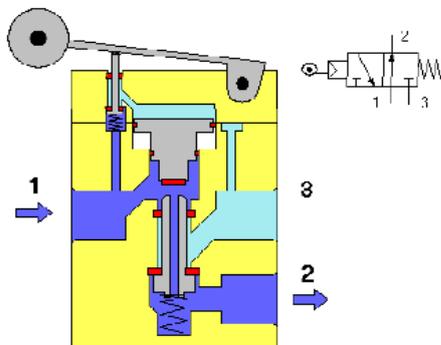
Válvula 3/2 inicialmente abierta accionada por rodillo
